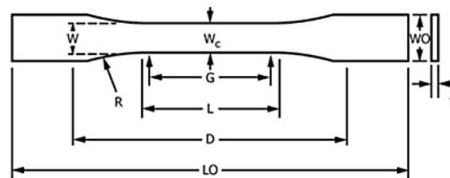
Corpo de prova Tipo I para ensaio de tração (ASTM 638-14).
